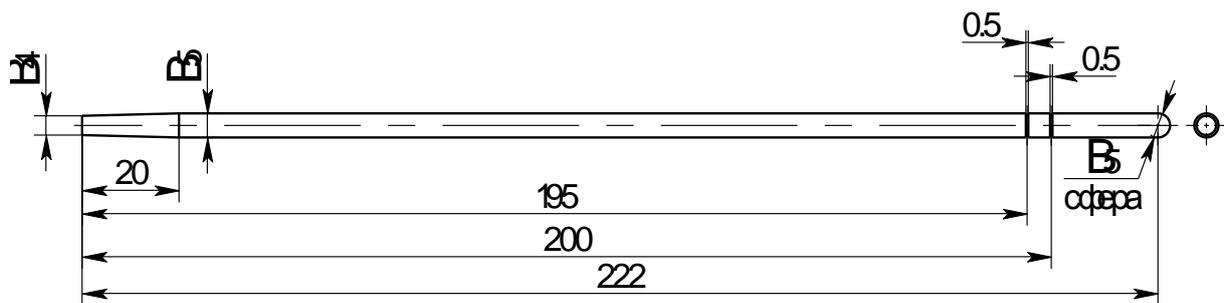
Заготовка для модели стержня модульного конструктора
